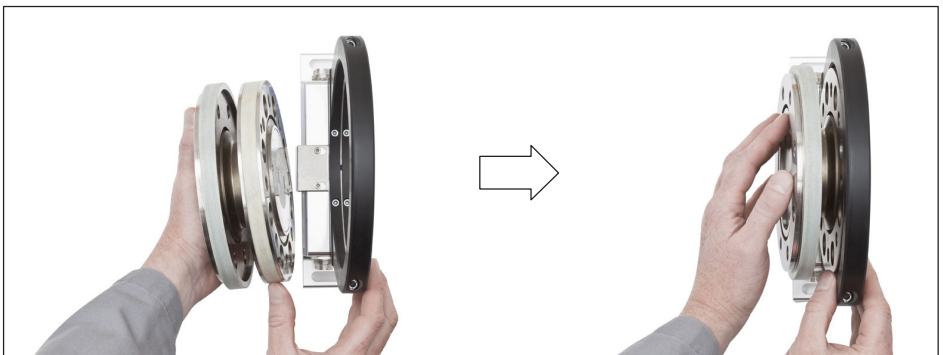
Ausrichten des Rotors mit dem Stator (ohne Referenzimpuls-Sensor) am Beispiel T40B. Gilt sinngemäß auch für T40MS
